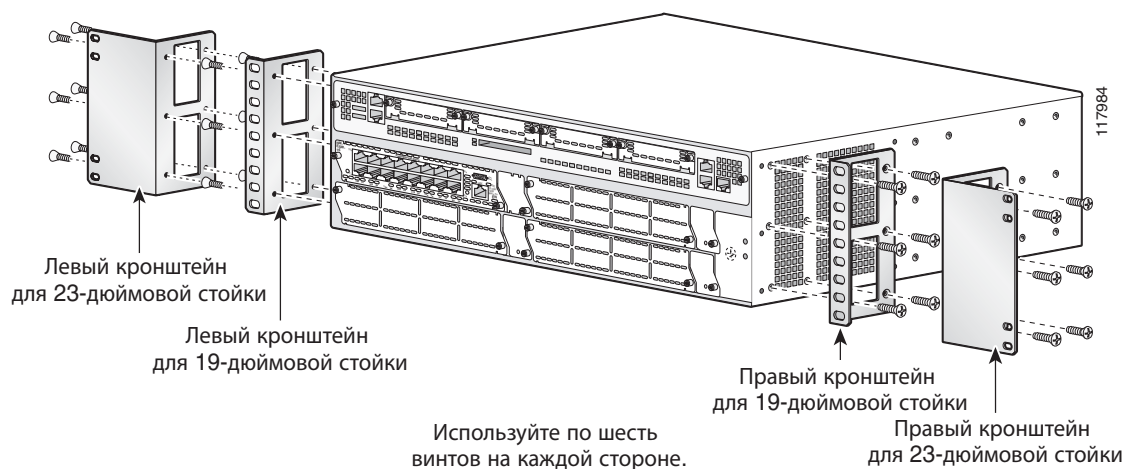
Крепление скоб для установки по центру передней панелью вперед
